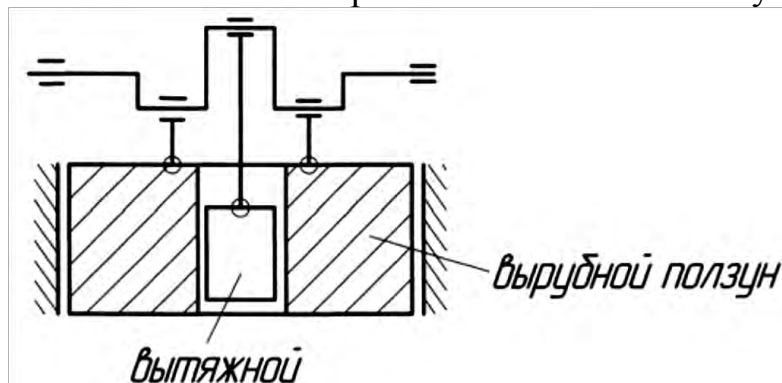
Схема вытяжного прессы двойного действия
